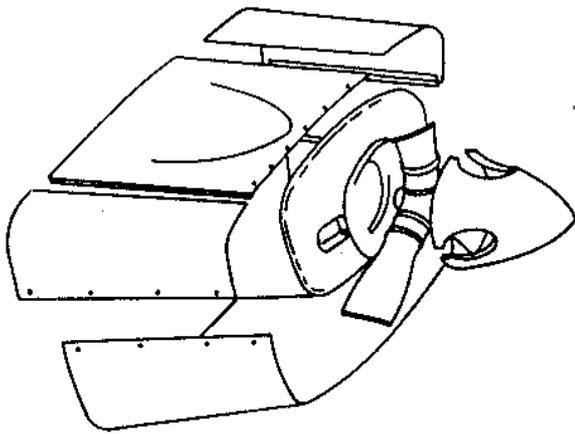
Carenagem para motor de cilindros horizontais opostos.
